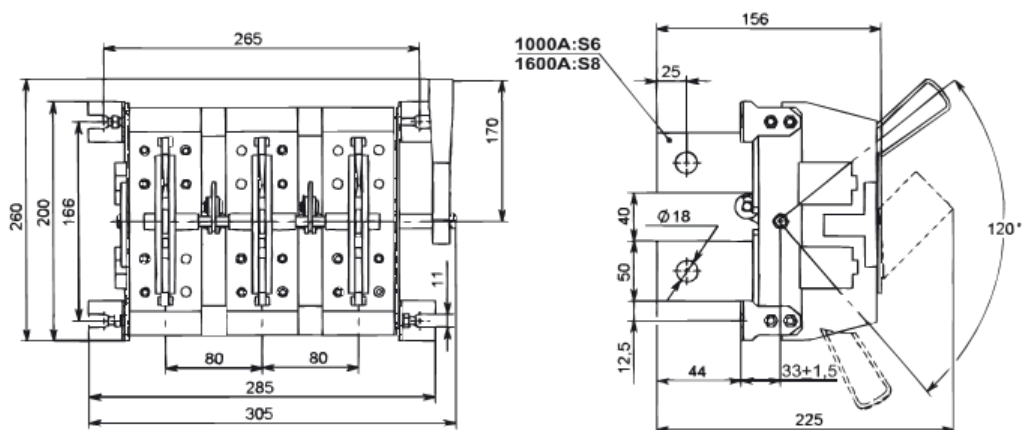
Разъединитель РЕ19–41(43)–32240–00 УХЛЗ с передней смещенной рукояткой, заднего присоединения шин
